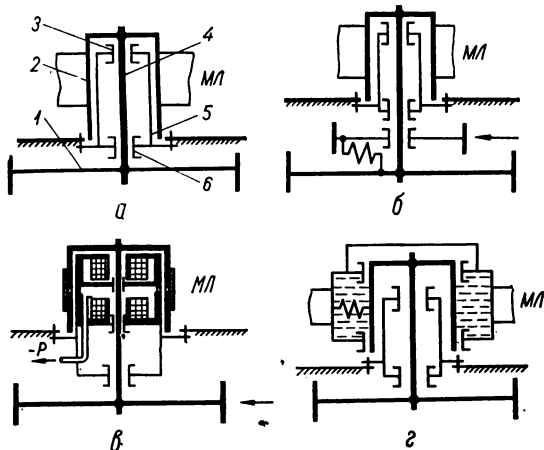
Кинематические схемы узлов ведущего вала исполнения V.
